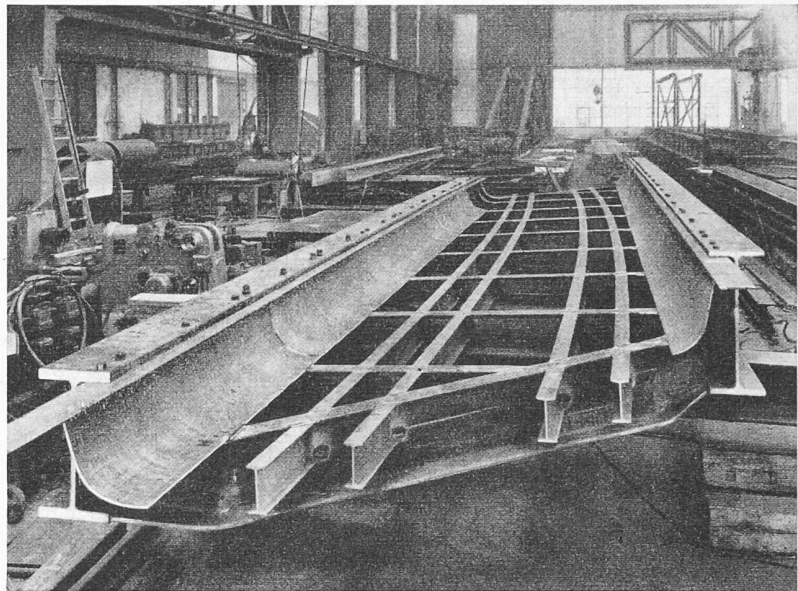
Einpassen der Trogbleche in der Werkstatt in Döttingen
